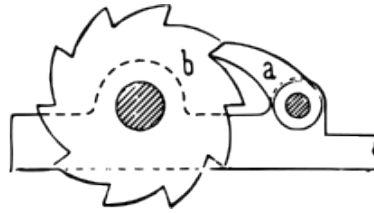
Храповий механізм, який складається з собачки (а) і зубчастого колеса (b)
